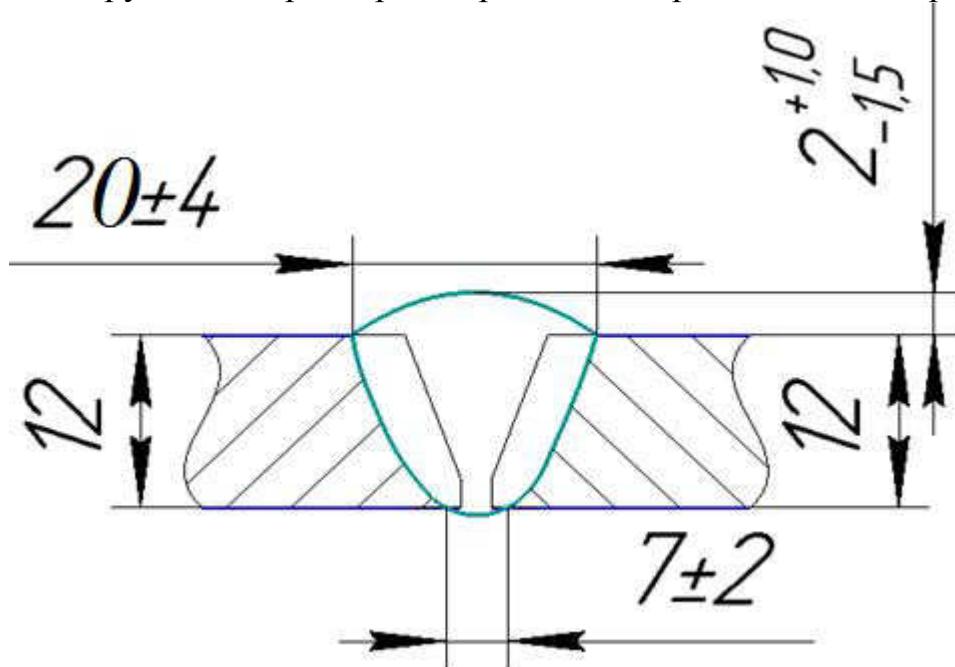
Конструктивные размеры сварного шва
